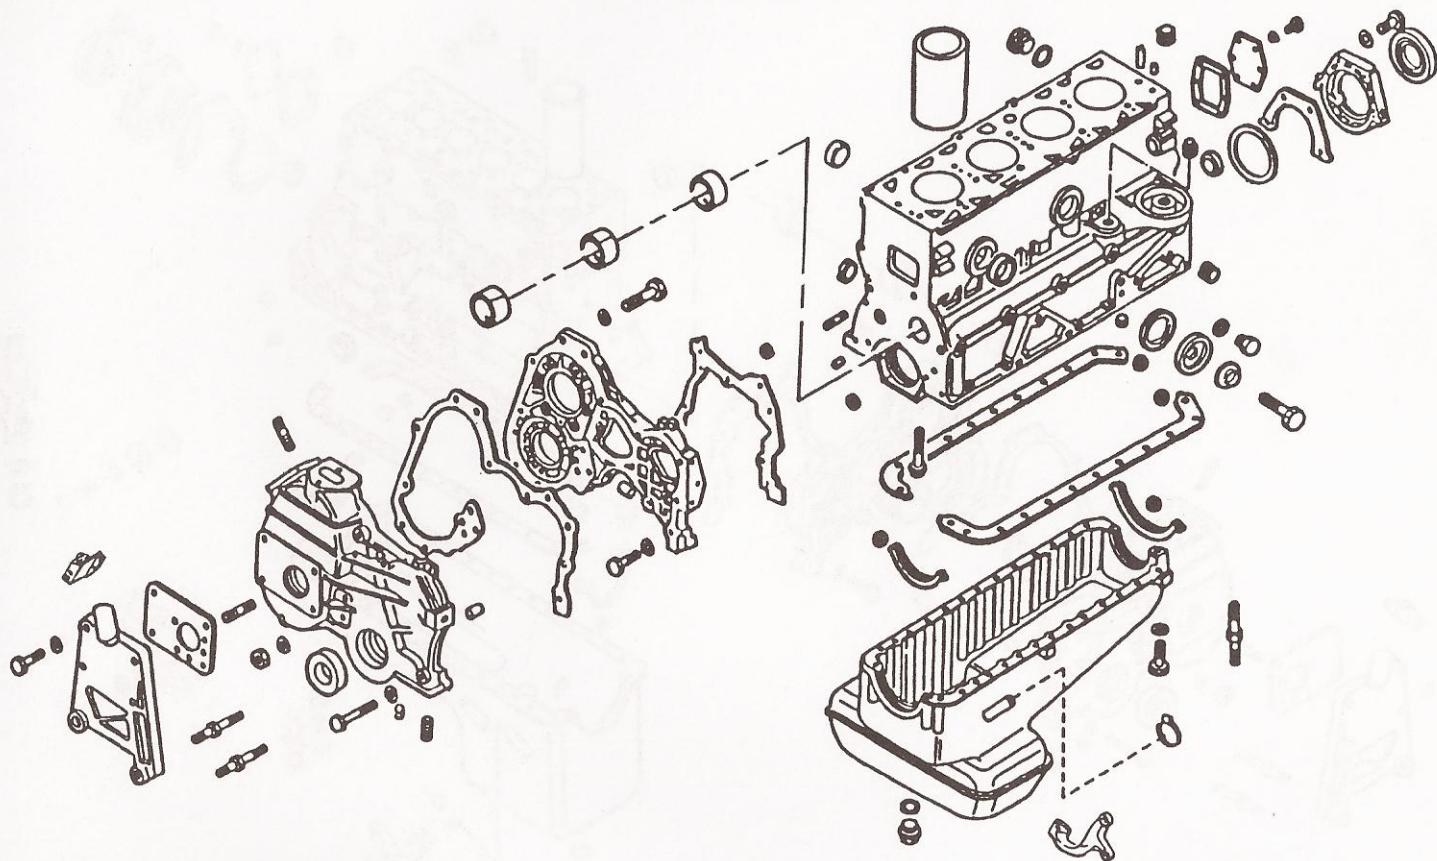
Блок цилиндров 4-цилиндрового двигателя.
